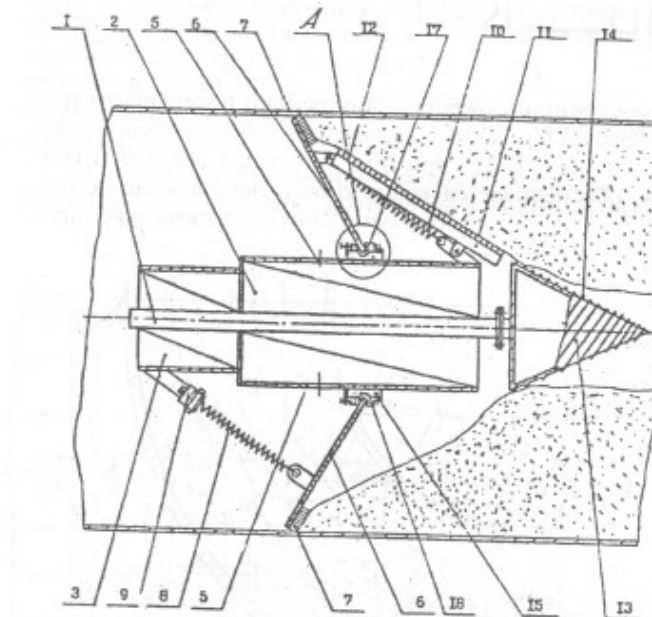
Общий вид очистного устройства для чистки магистральных, цеховых и межцеховых трубопроводов, где 1 – вал; 2 – первая турбинка; 3 – вторая турбинка; 4 – ступенчатый корпус; 5 – отверстия; 6 – лепестки; 7; 12; 14 – очистные элементы; 8, 10 – пружины; 9 – натяжной узел; 11- щетки; 13 – конусный наконечник; 15 – внутреннее кольцо; 17 – ролики; 18 – наружное кольцо.
